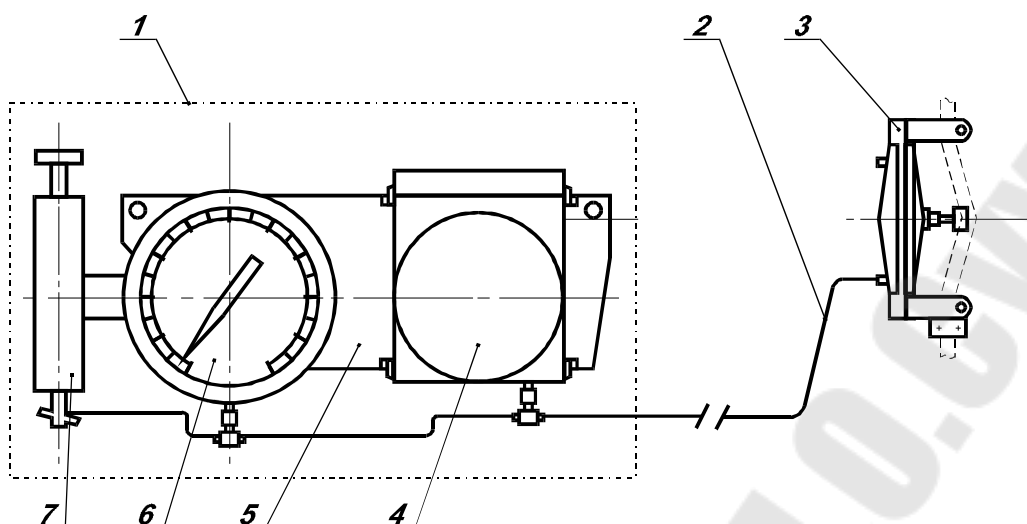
Монтажная схема гидравлического индикатора веса на жесткой раме: 1 – блок вторичного привода; 2 – трубопровод соединительный; 3 – трансформатор давления; 4 – манометр самопишущий; 5 – рама; 6 – указатель; 7 – пресс-бачок
